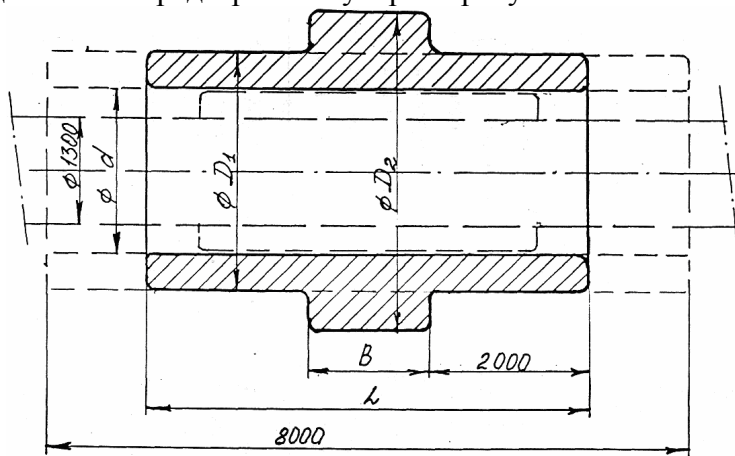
Эскиз ступенчатой трубной поковки для изготовления днищ при различных операцияхковки
